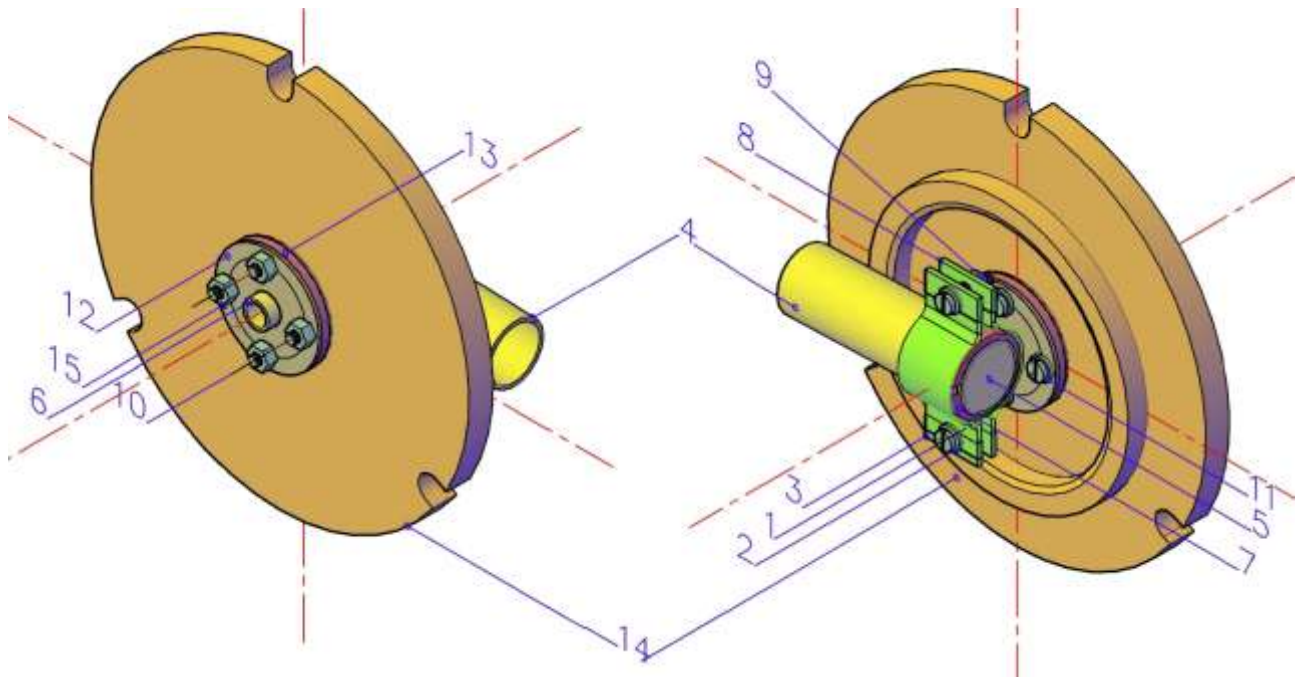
Вузол кріплення досліджуваної насадки на торцевій кришці напірного бака: 1,10 – болти; 2, 11, 12 – шайби; 3, 8 – монтажні хомути; 4 - фрагмент РТ; 5 – заглушка на торці РТ; 6 – вихідна насадка; 7, 13 - гумові прокладки; 9, 15 – гайки; 14- торцева кришка напірного бака (вигляд на торцеву кришку з зовнішнього та внутрішнього боків) [80]
